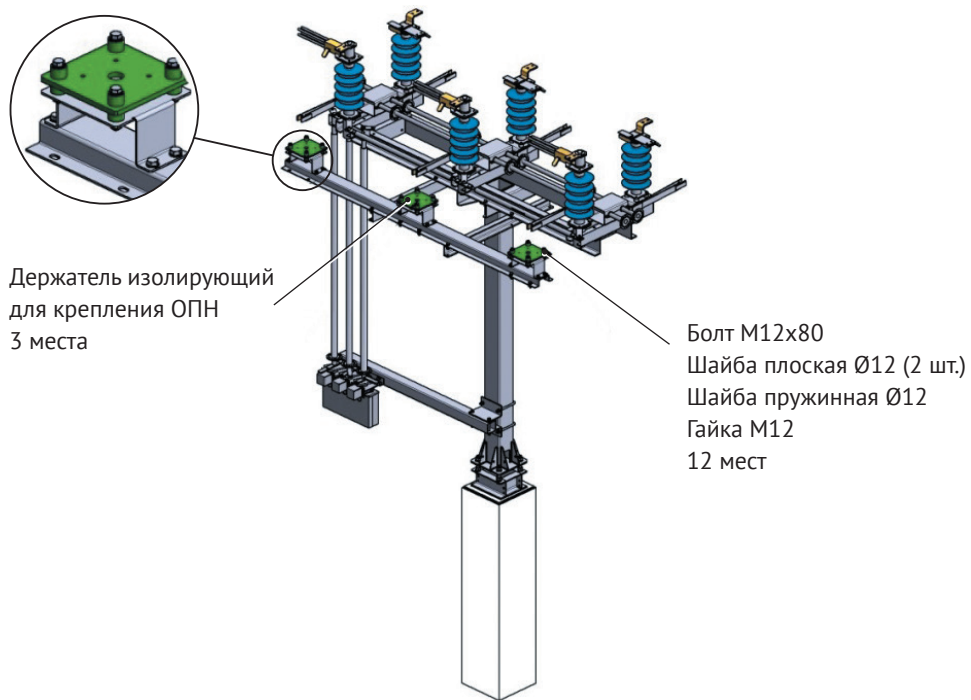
Установка изолирующих держателей ОПН-РК-35
